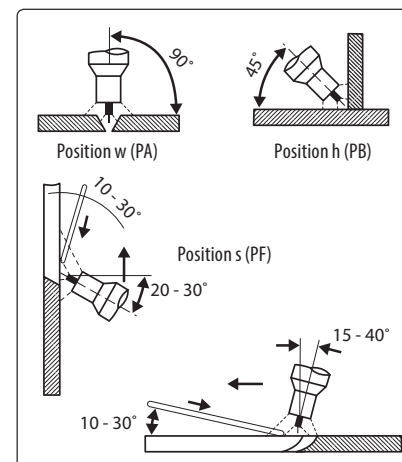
, Prinzip der TIG-Methode mit Einsatz vom Schweißstab
